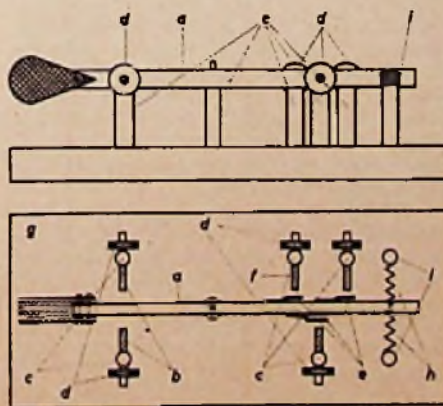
Morsetaste T. a) Geber, b) Abstandsschraube, c) Ständer, d) Justiermutter, e) Federkontakt, f) Kontaktschraube, g) Grundplatte, h) Spiralfeder, i) Befestigung der Spiralfeder
